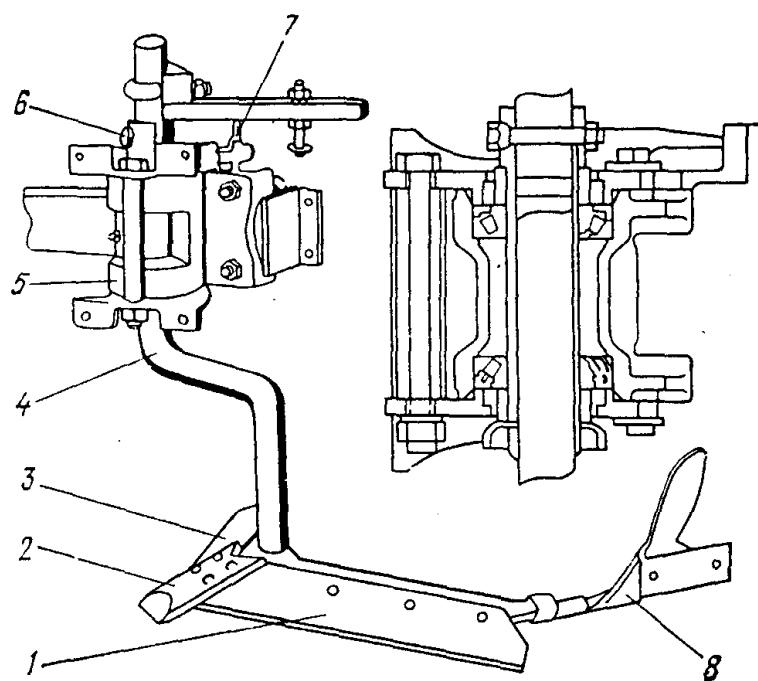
Поворотная лапа приспособления ПРВМ-11.000:
